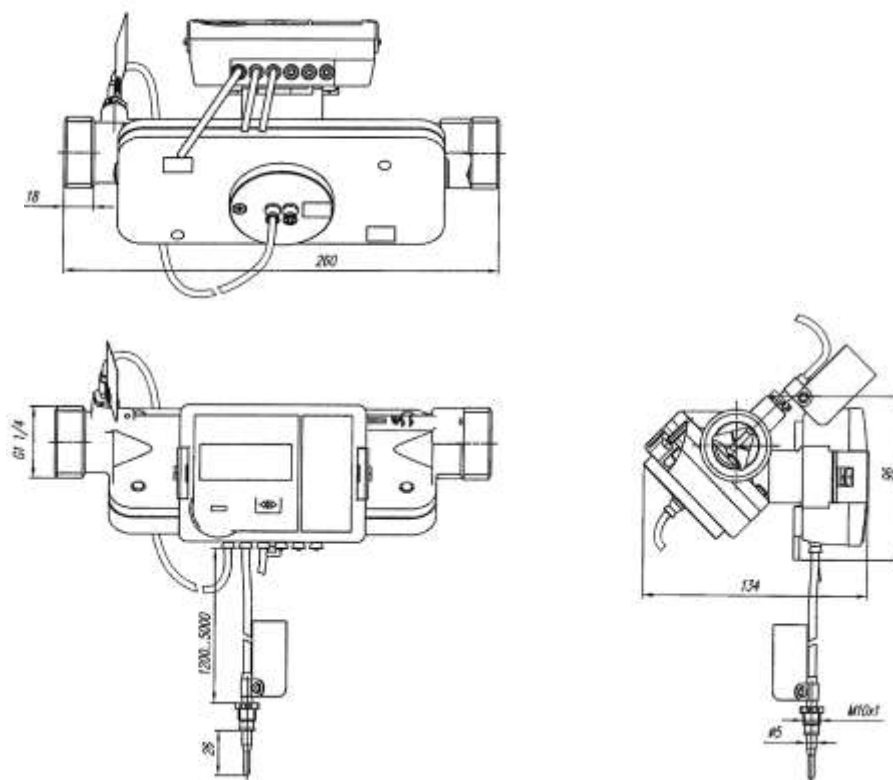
Присоединительный размер к трубопроводу G1 1/4", длина L=260 мм
